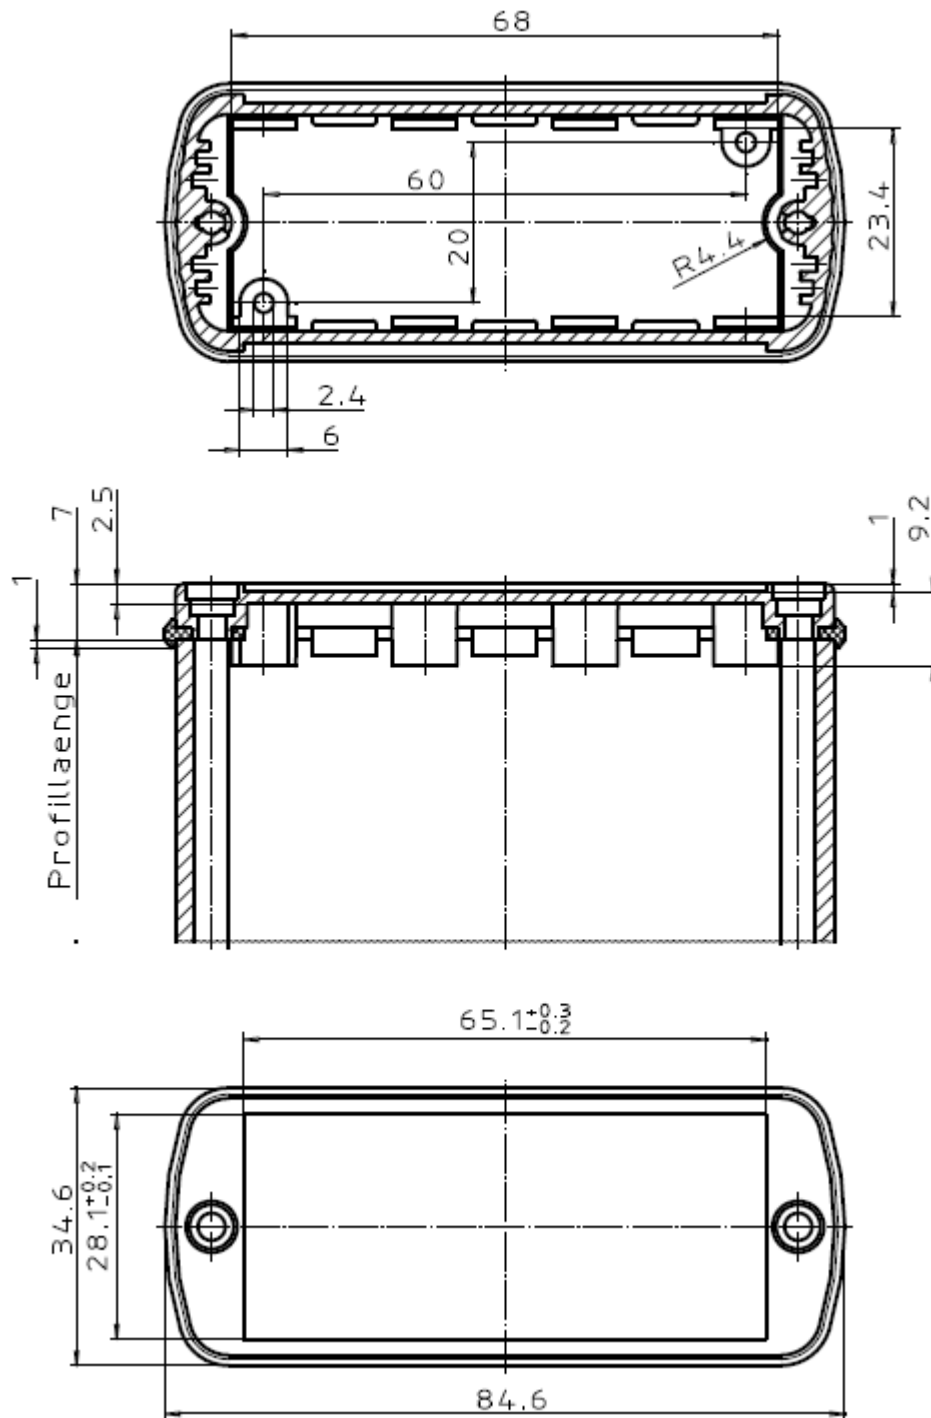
а. Сборочный чертеж крышки корпуса.
